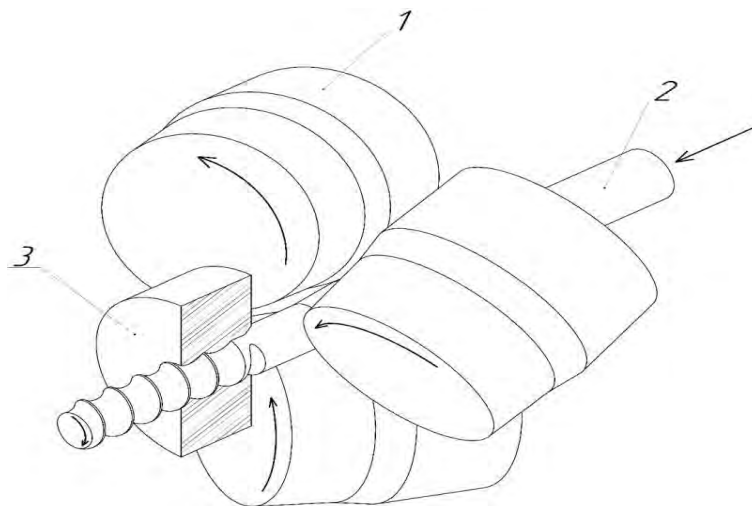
Совмещенный способ получения арматурного профиля: 1 – прокатные валки, 2 – заготовка, 3 – матрица
